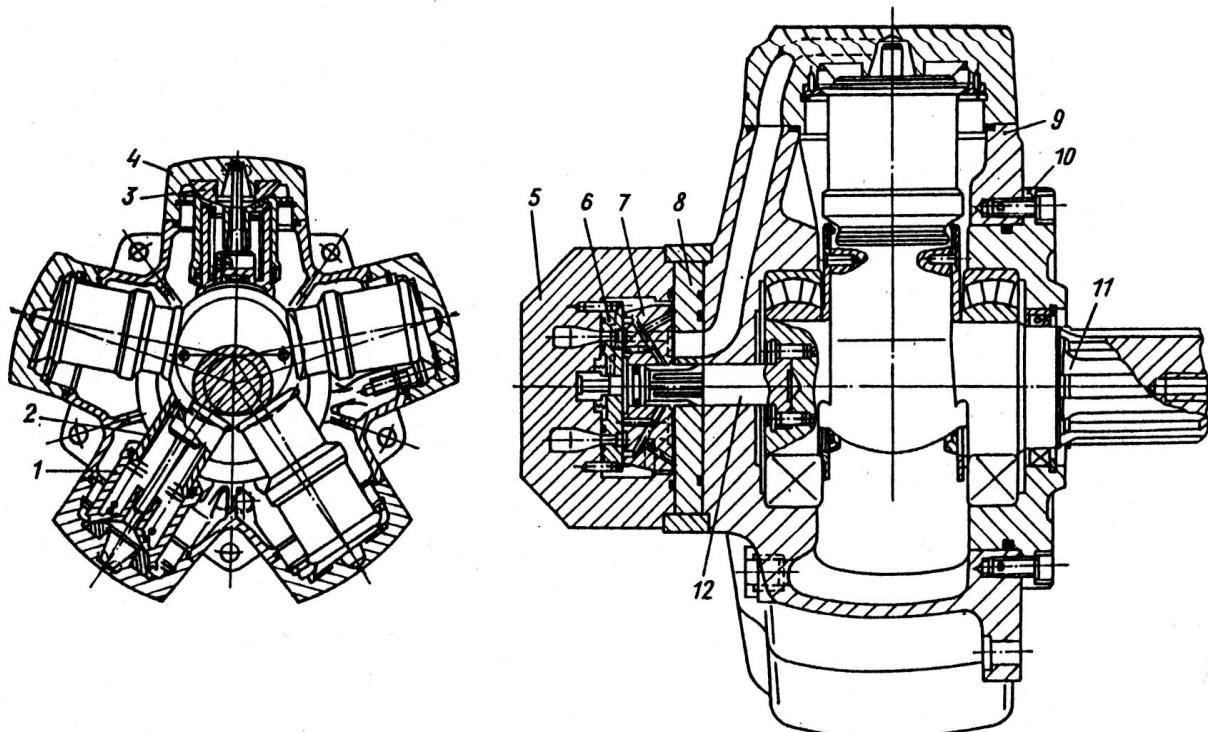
Радиально-поршневой гидромотор типа МР:
